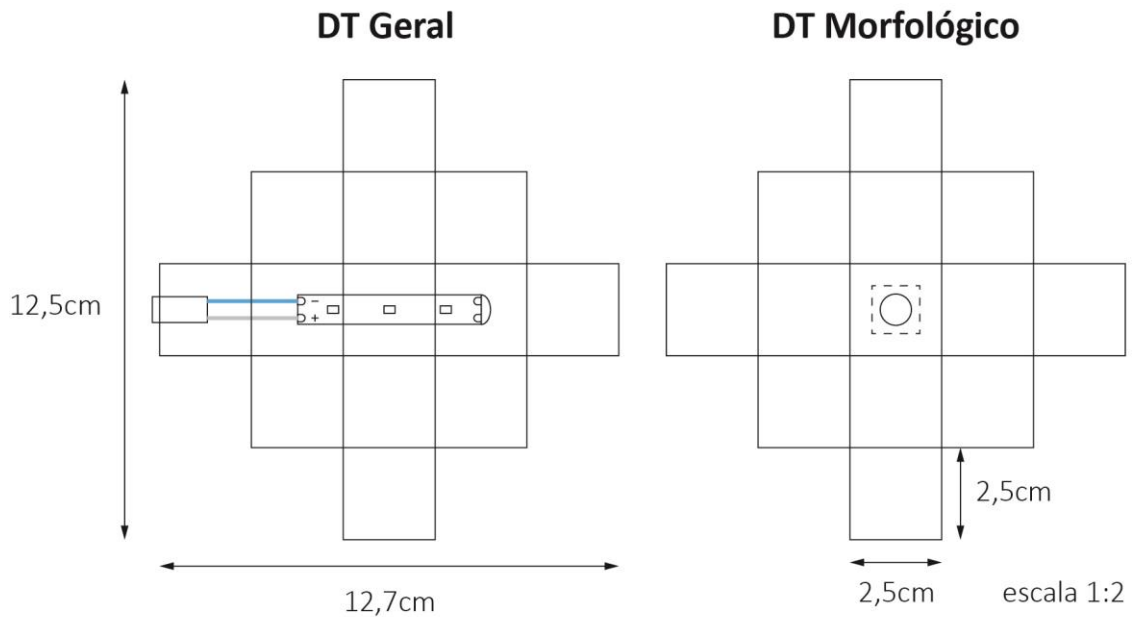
Desenho técnico de corte e vinco do Abajur Pequeno
